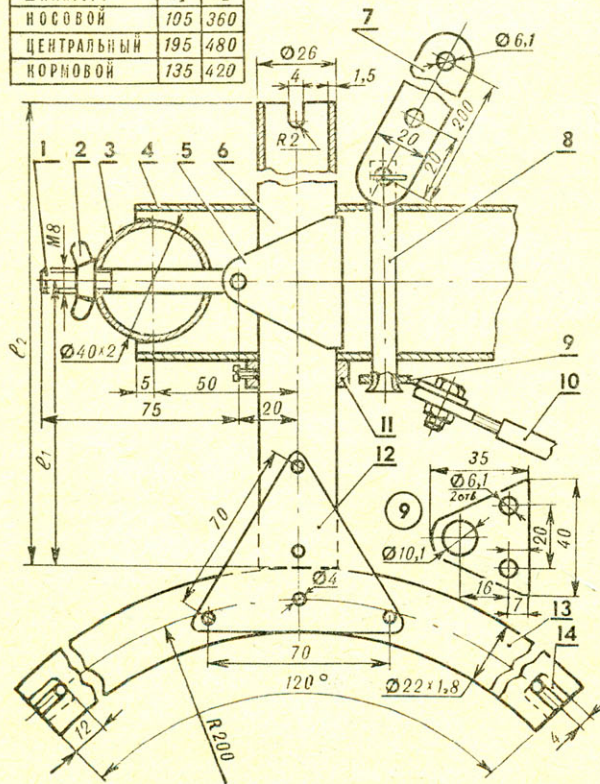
Типовой соединительный узел шпангоута, стрингера и поперечной балки:
